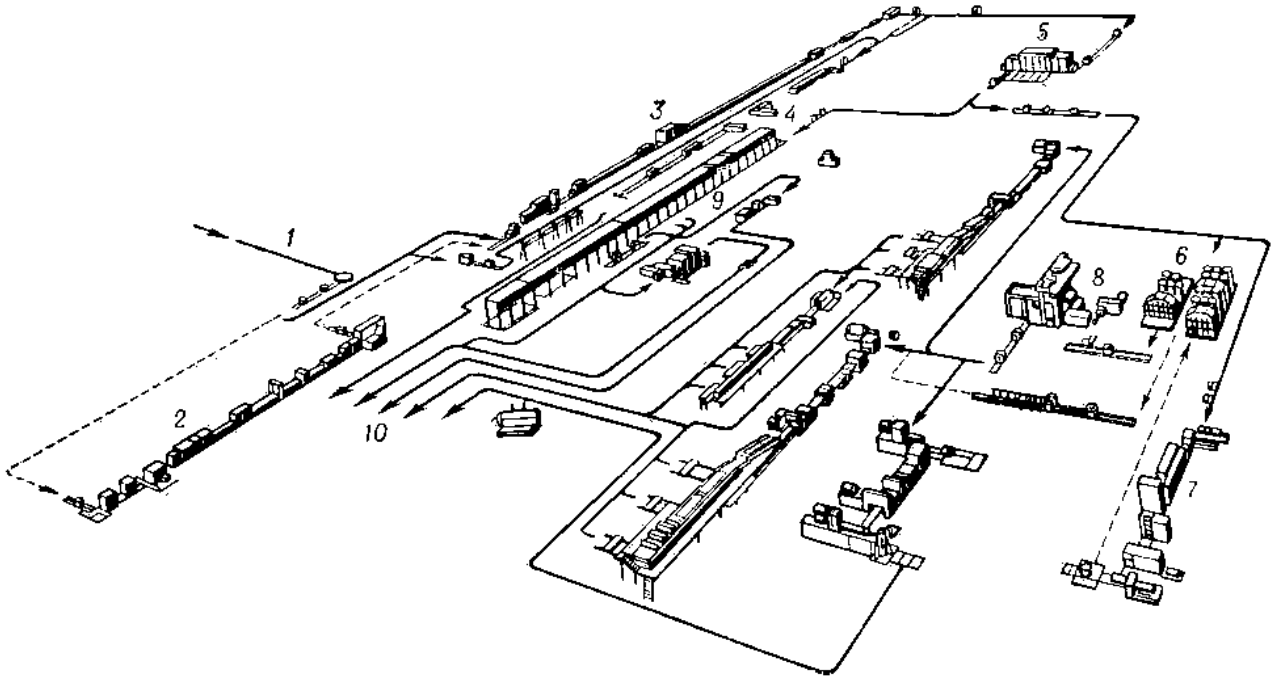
Технологічна схема цеху холодної прокатки для виробництва листів: 1 - конвеєр гарячекатаних рулонів; 2 - агрегат нормалізації; 3 - безперервно-травильний агрегат; 4 - агрегат комбінованого різання; 5 - безперервний стан холодної прокатки; 6 - термічне відділення; 7 - агрегат нанесення захисного покриття; 8 - дресирувальний стан; 9 - безперервно-цинкувальний агрегат; 10 - відділення упаковки готових продуктів.
